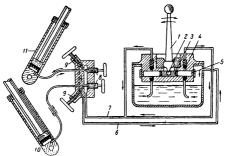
Схематический чертеж снегоочистителя Д-151.
